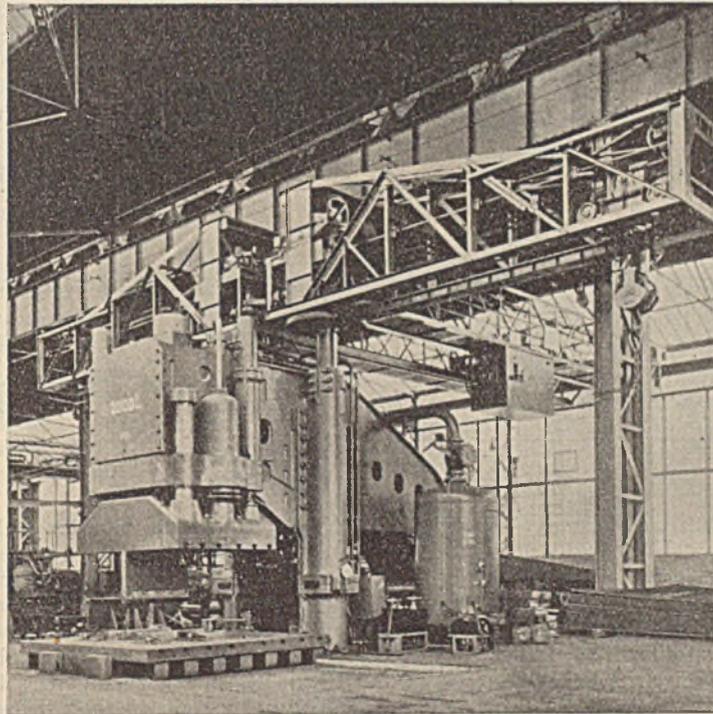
Geschweißte 2000-t-Schiffbaupresse.
